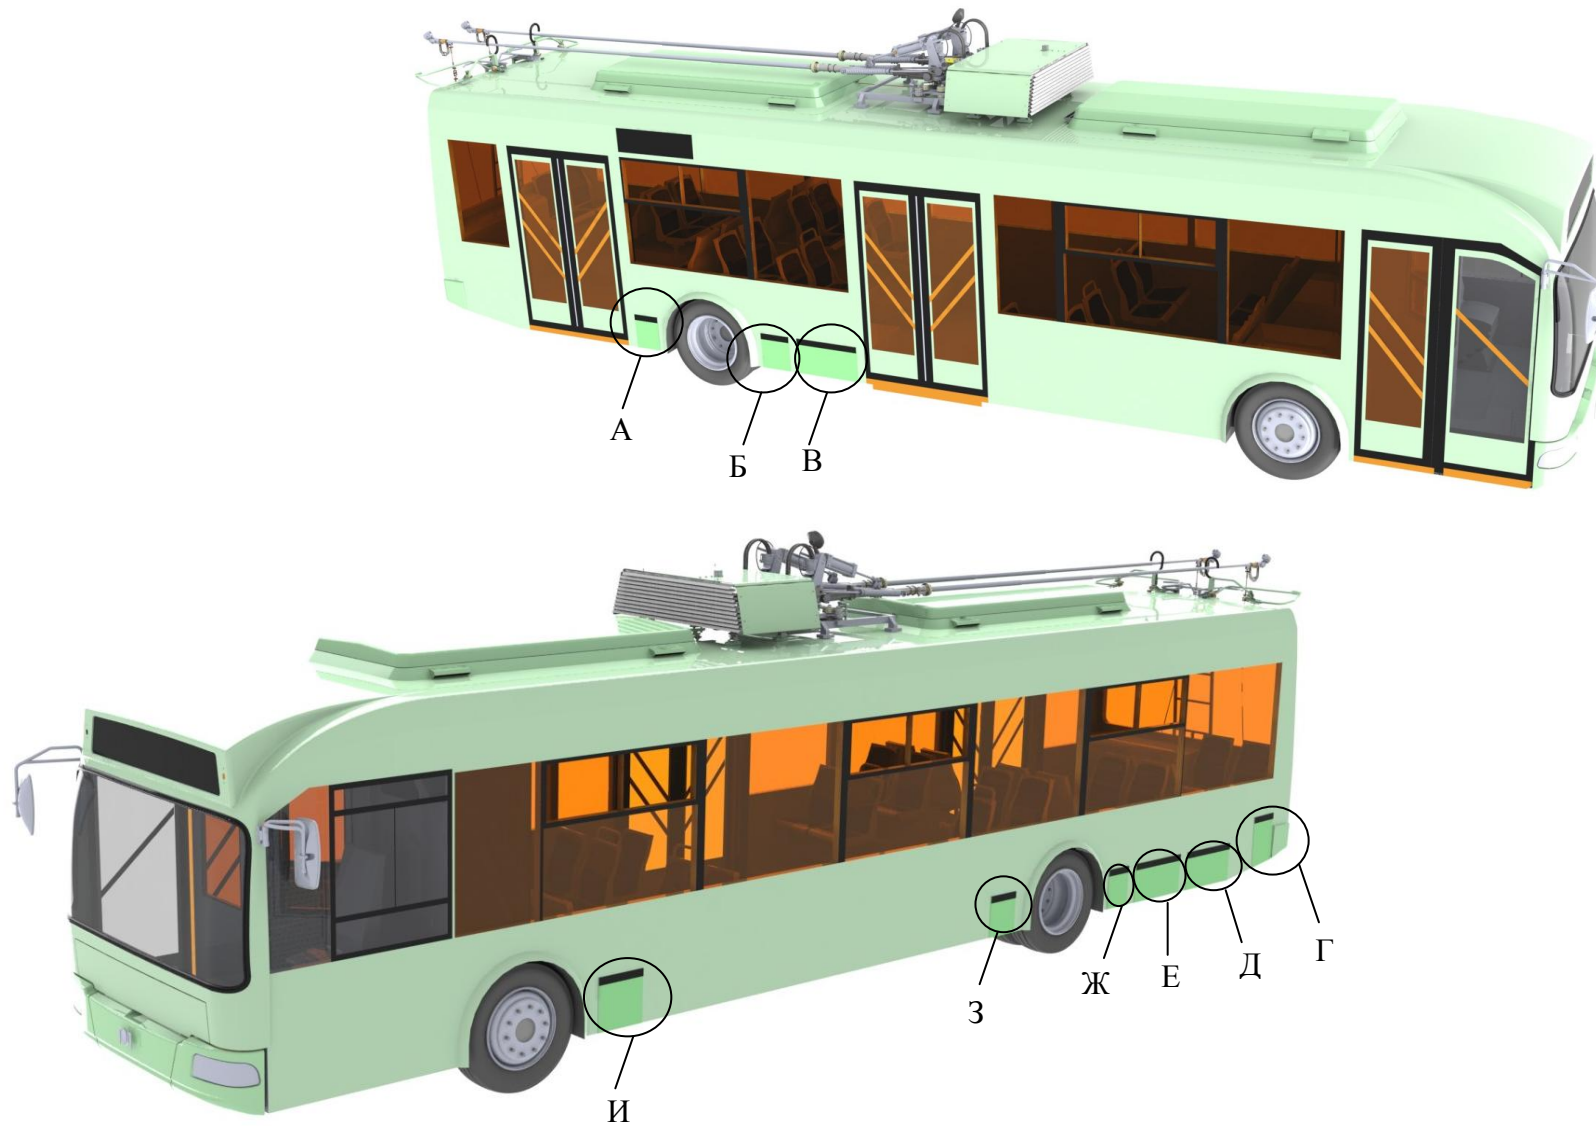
(лист 1 из 10) – Установка люков боковых АКСМ 321-132100.000
